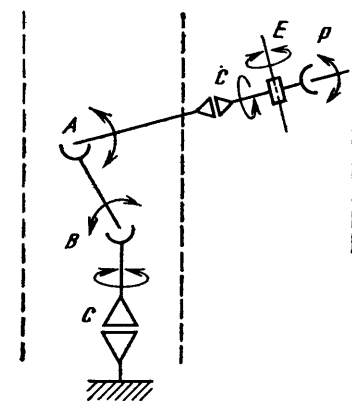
Пример кинематической схемы шестизвенного робота-маляра
